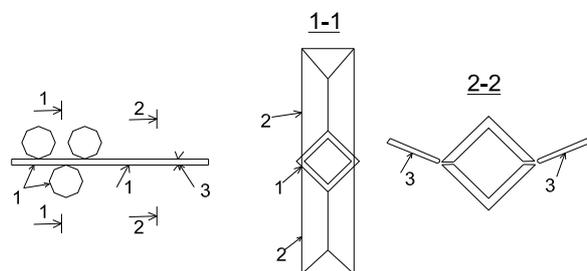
Схема образования прямоугольных сварных труб из прокатных уголков: 1) уголки, образующие трубу; 2) валки с выемками; 3) электроды и сварочный автомат
